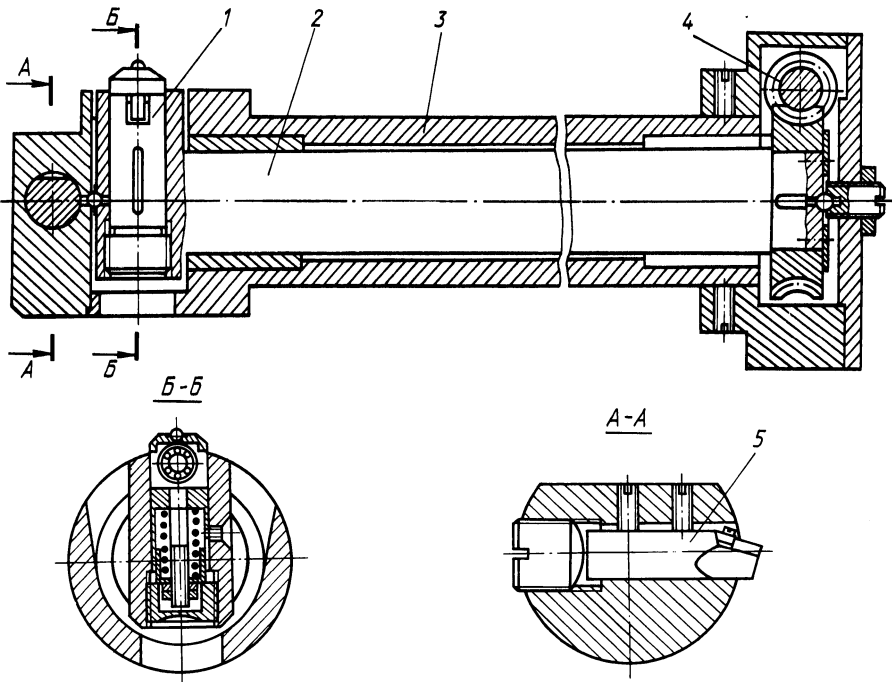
Комбинированный инструмент для осуществления адаптивного управления точностью обработки
